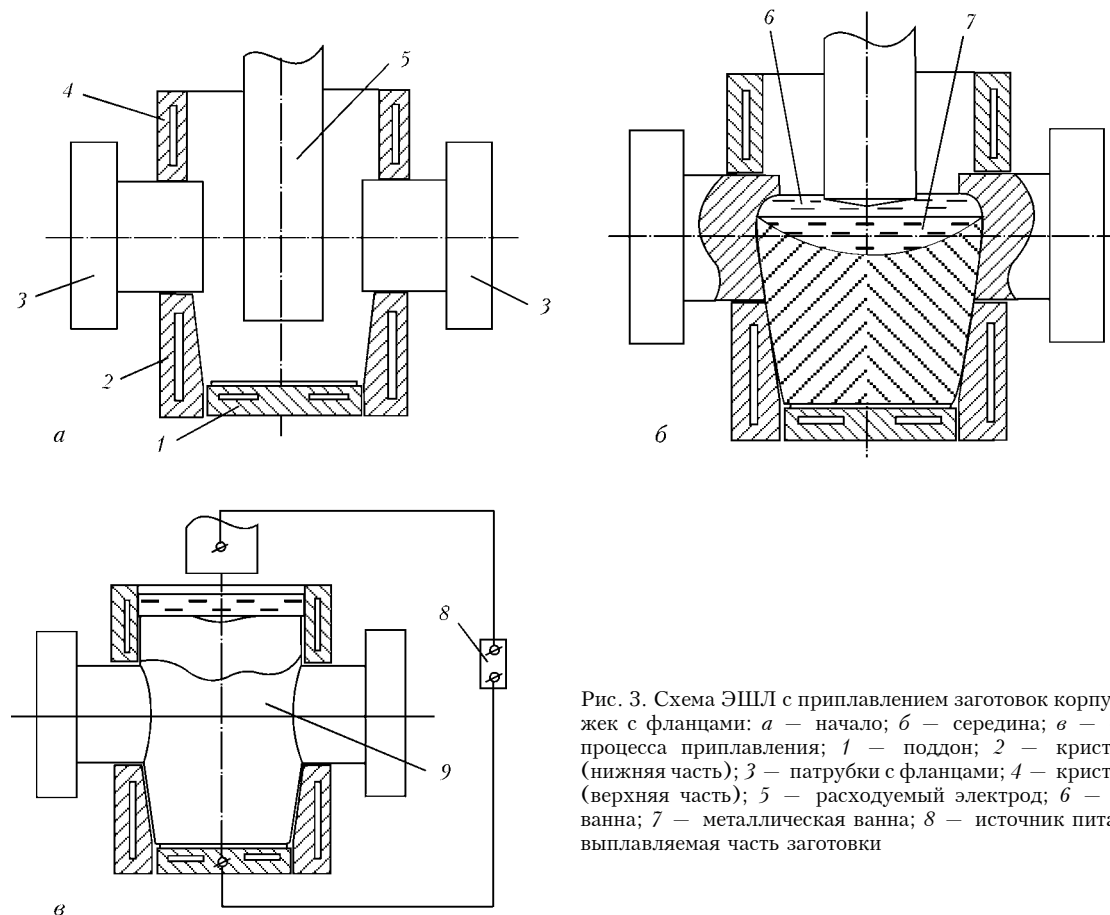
Схема ЭШЛ с приплавлением заготовок корпусов задвижек с фланцами: *а* – начало; *б* – середина; *в* – окончание процесса приплавления; 1 – поддон; 2 – кристаллизатор (нижняя часть); 3 – патрубки с фланцами; 4 – кристаллизатор (верхняя часть); 5 – расходный электрод; 6 – шлаковая ванна; 7 – металлическая ванна; 8 – источник питания; 9 – выплавляемая часть заготовки
